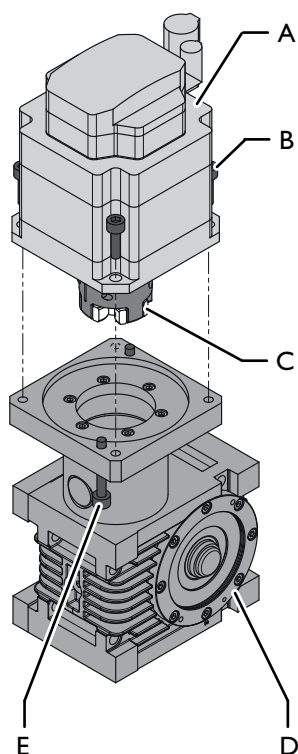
Удалить мотор: Блок редуктора Güdel
